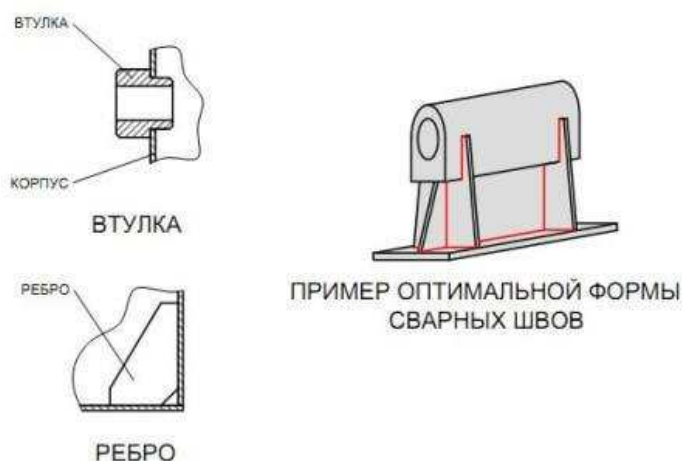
Элементы сварных деталей из сортового проката
